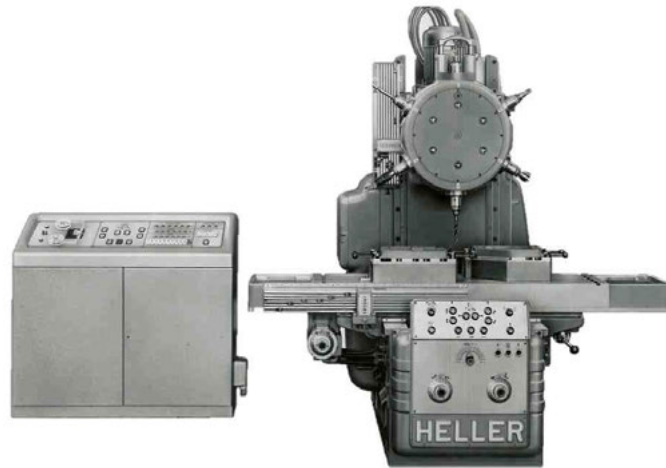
Heller SBR 32 für die 6. Werkzeugmaschinen-Ausstellung 1959 in Paris¹¹³³
